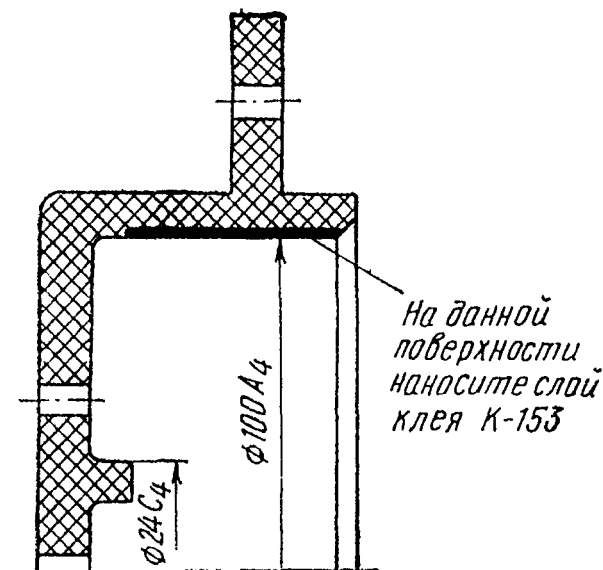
Фланец крепления контактов обогрева обтекателя втулки винта
